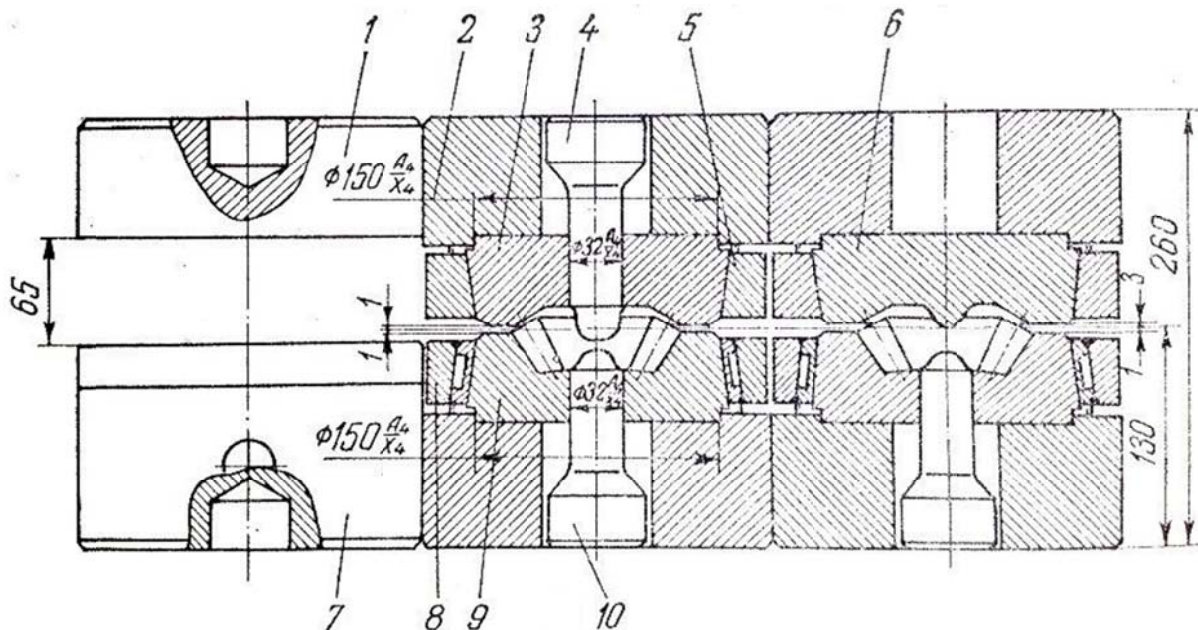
Эскиз штампа для объемной штамповки поковок «Сателлит»
